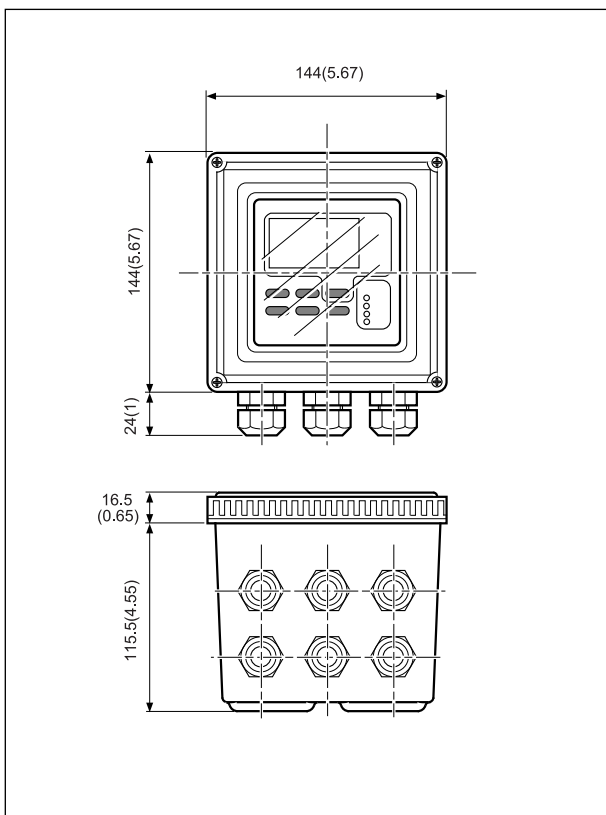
Размеры корпуса и расположение уплотнителей
